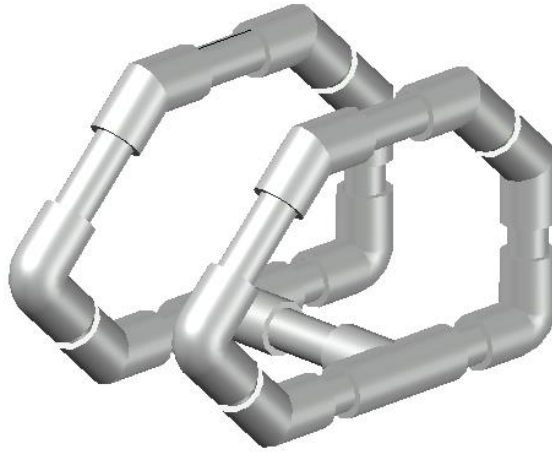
Vista en isométrico del ensamblaje tubular del prototipo.
